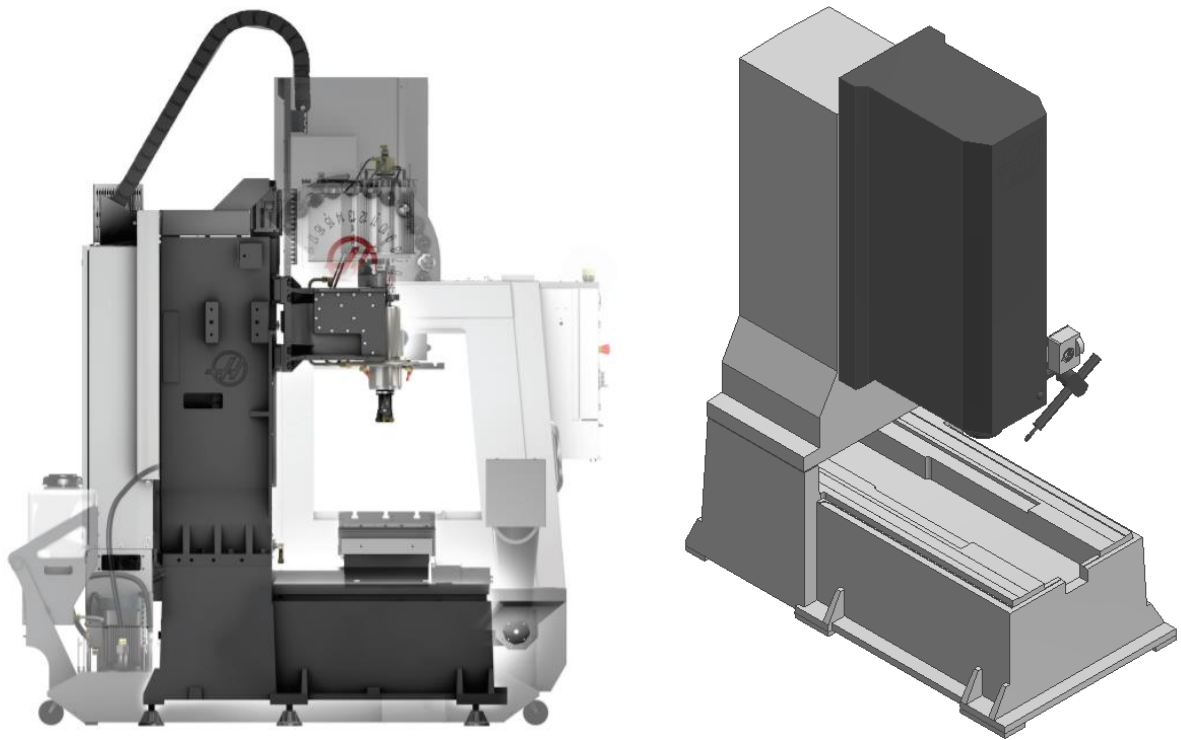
Зовнішній вигляд верстату Haas VF-2 і 3D-модель станини
